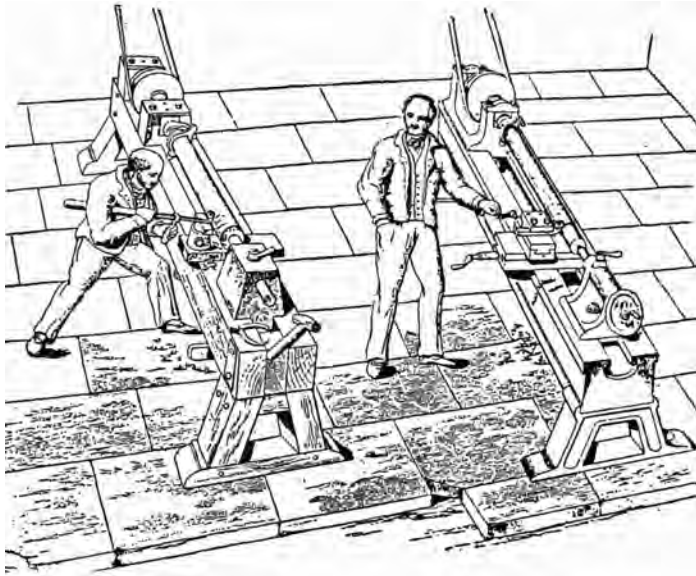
Zeichnung von James Nasmyth 1841, die den Unterschied zwischen «Hand-Werkzeug-Technik» und «Maschinen-Werkzeug-Technik» illustriert. An der linken (aus Holz gebauten) Drehbank bearbeitet der Dreher das Werkstück mit einem aufgelagerten Handdrehmeissel. An der rechten Drehbank mit gusseisernem Rahmen erzeugt der Dreher nur die Vorschubbewegung mit einer Handkurbel. (Benad-Wagenhoff, Paulinyi und Ruby 1993, S. 194)
